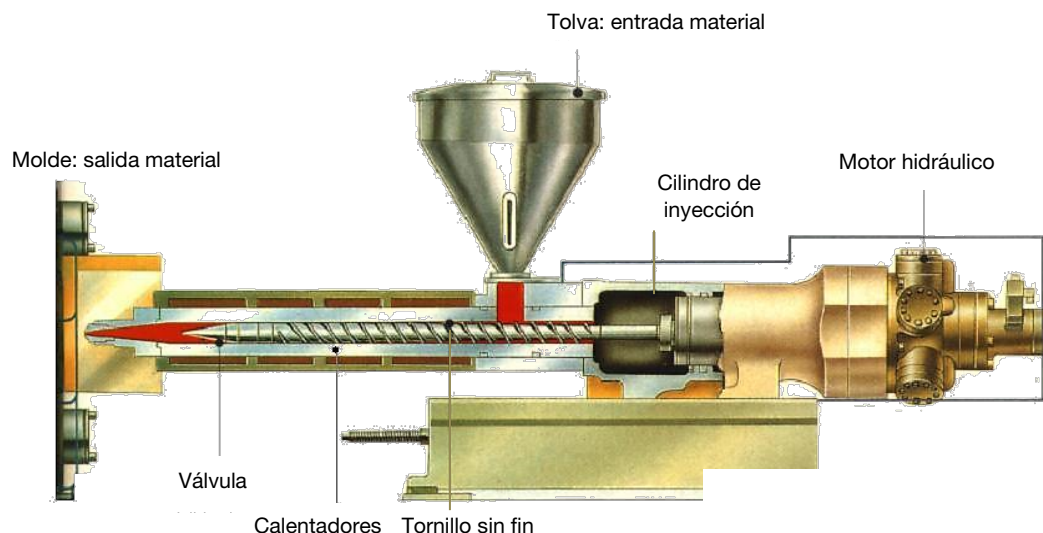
Sección transversal de una máquina de moldeo por inyección [55]
